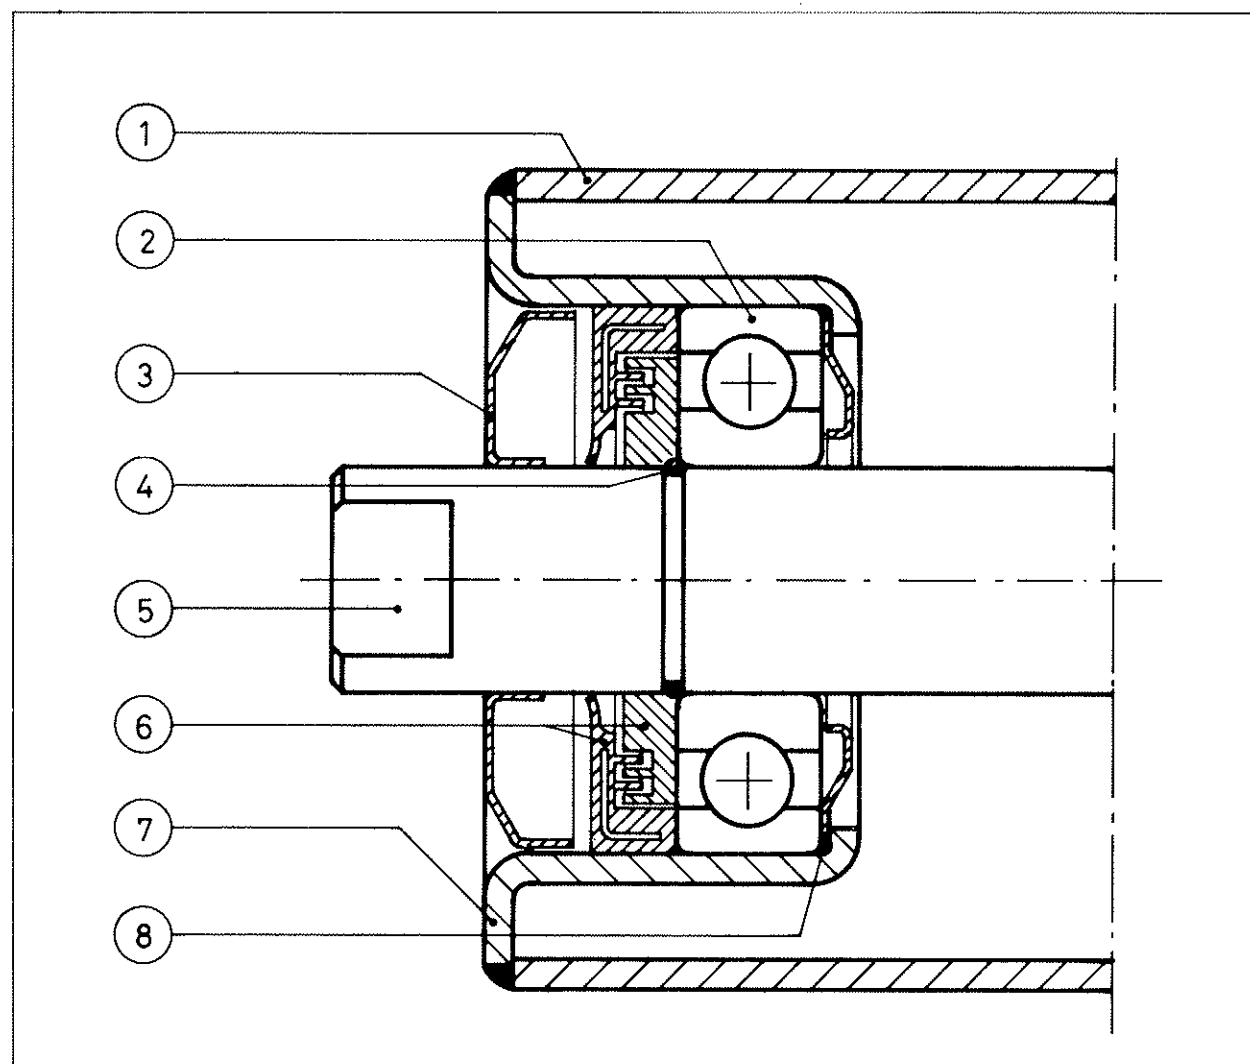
Soldadura interior para diámetro superior a 108 mm.
